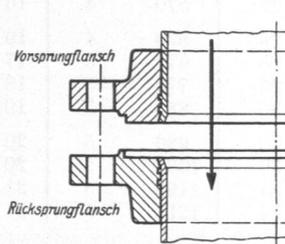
Flansch mit Eindrehung für Flachdichtung DIN 2513.
